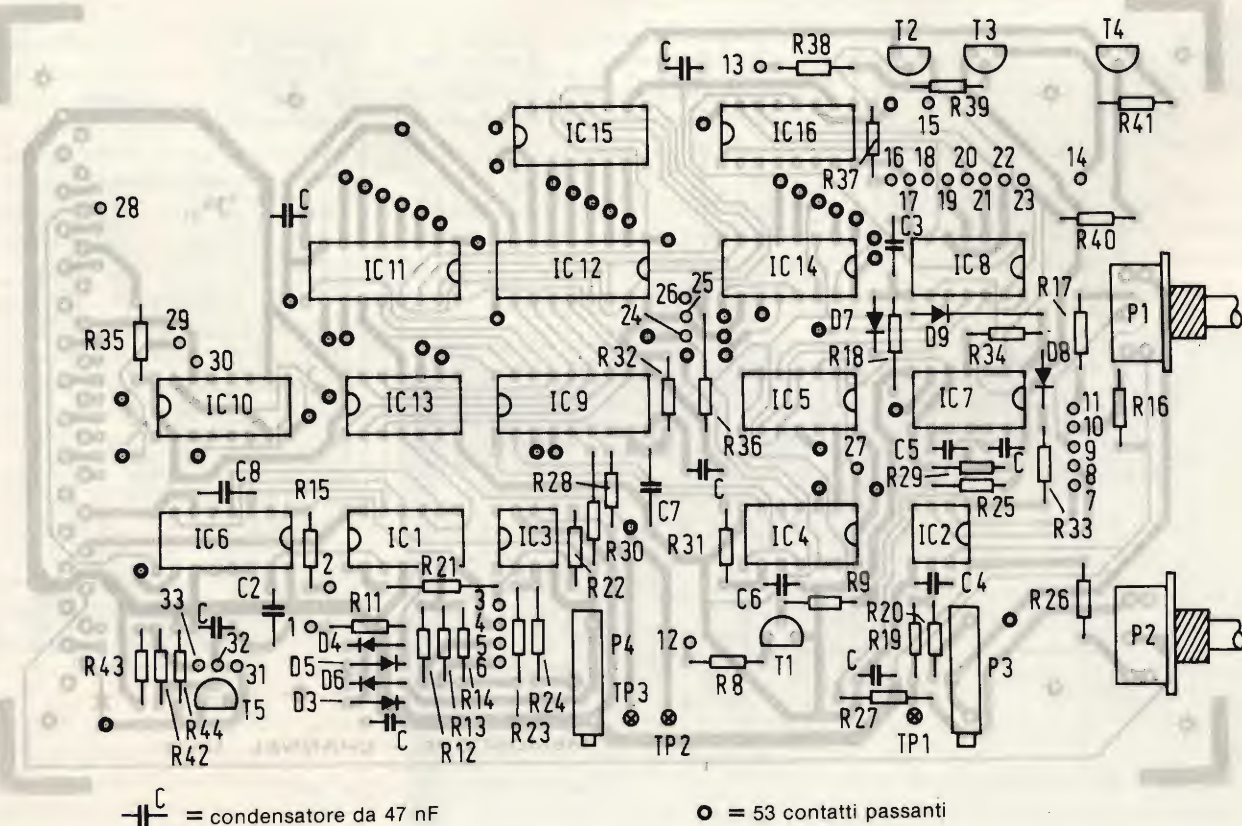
Per facilitare il montaggio, la disposizione dei componenti è stampata contrapposta alla serigrafia delle piste del lato saldature.
